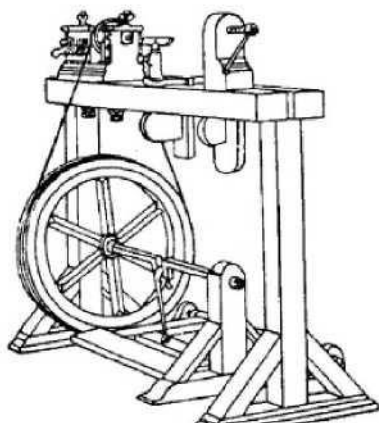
Токарний верстат з кривошипним приводом та маховиком
